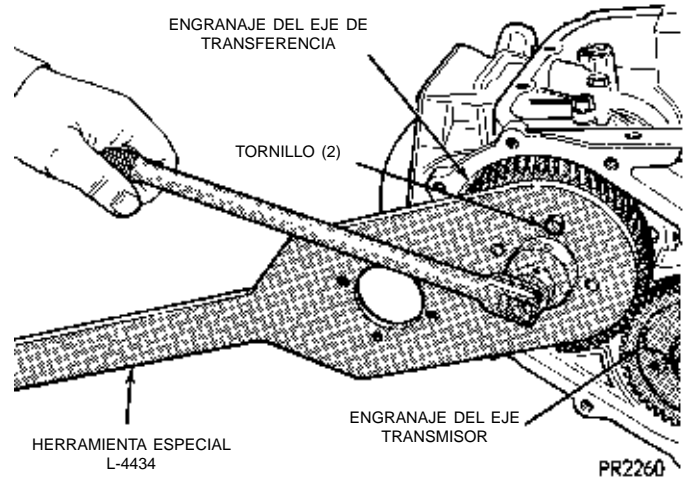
Desmontaje de la tuerca de retén del engranaje del eje de transferencia
